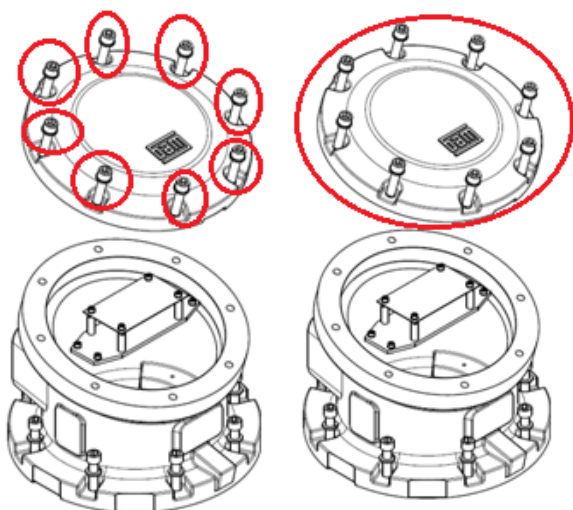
Демонтаж крышки клеммной коробки
